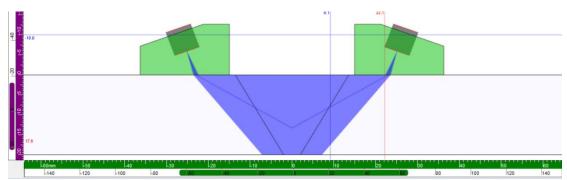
(T=20MM) 单 V 焊缝波束的覆盖范围
